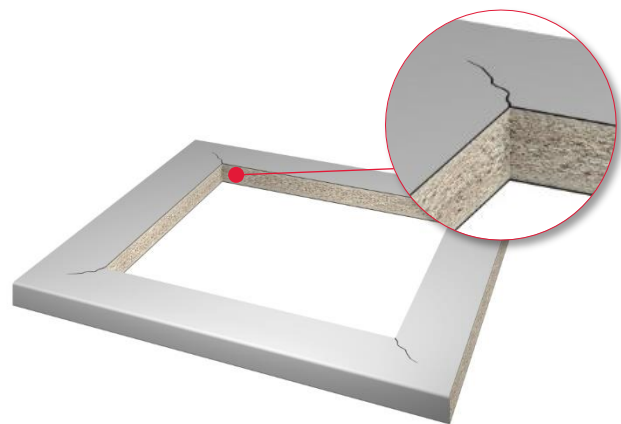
FALSCH – eckiger Ausschnitt mit zu kleinem Radius
